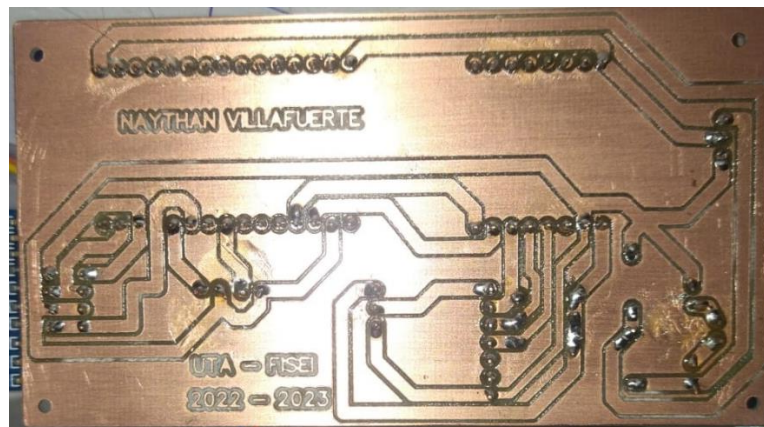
Soldaduras de la placa del dispositivo electrónico
